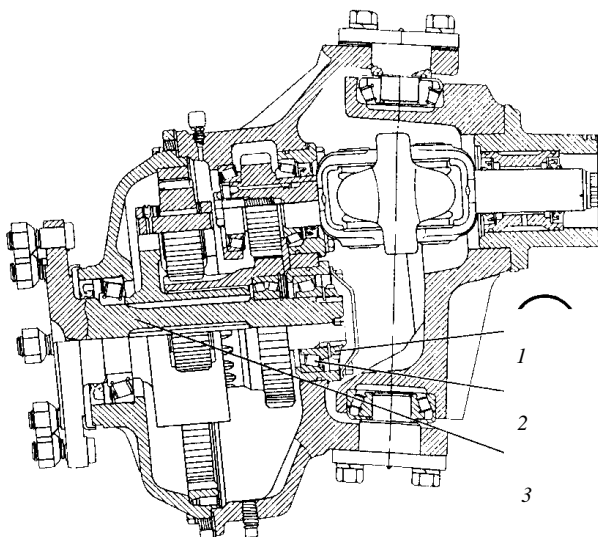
Проверка зазоров в подшипниках передних колес:
